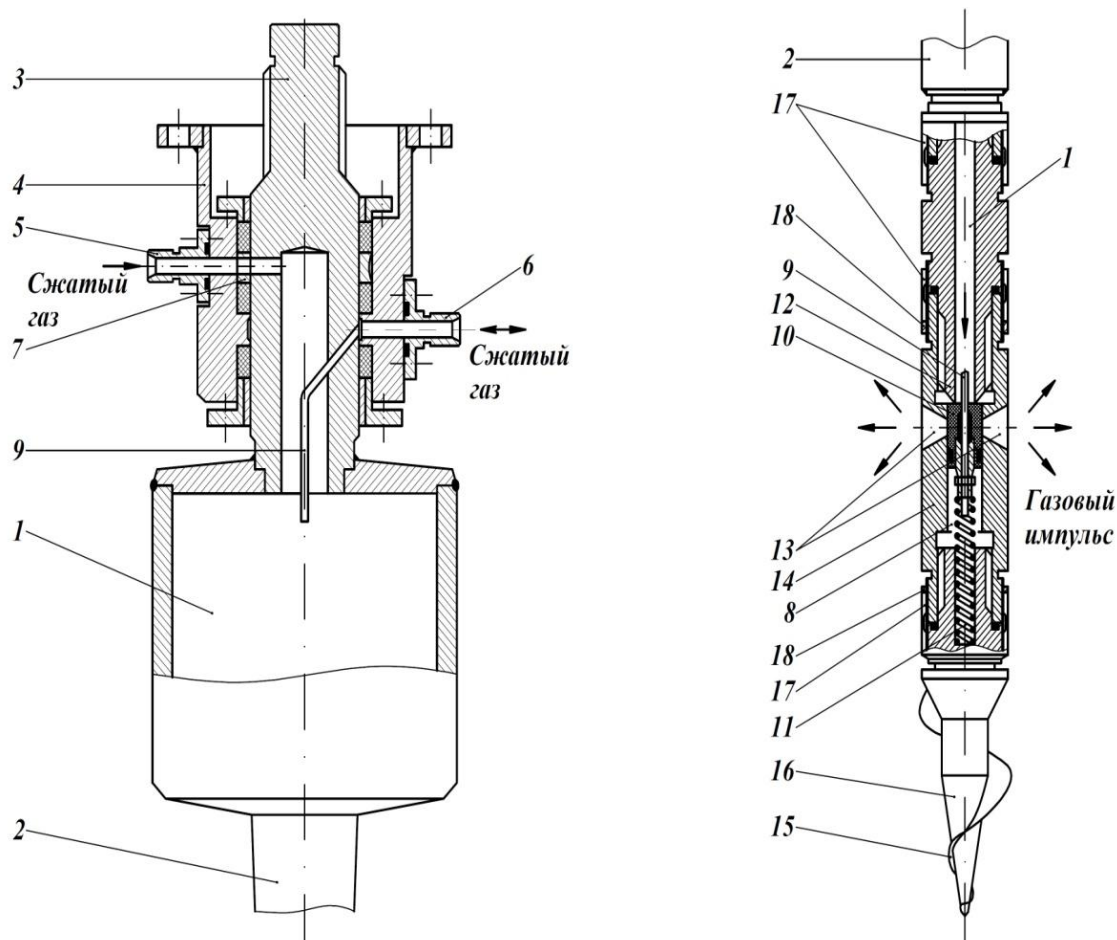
Газораспределительный узел с рабочей камерой (а)
